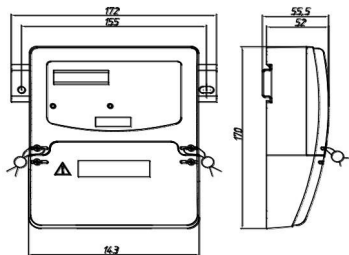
Загальний вигляд лічильника ЦQ36804-U у корпусі P32
